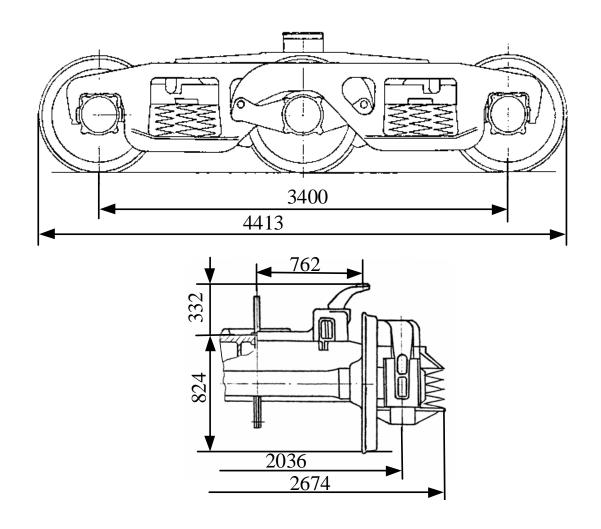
Назначение: для подкатки под струги – снегоочистители СС-1М и весоповерочные вагоны,
